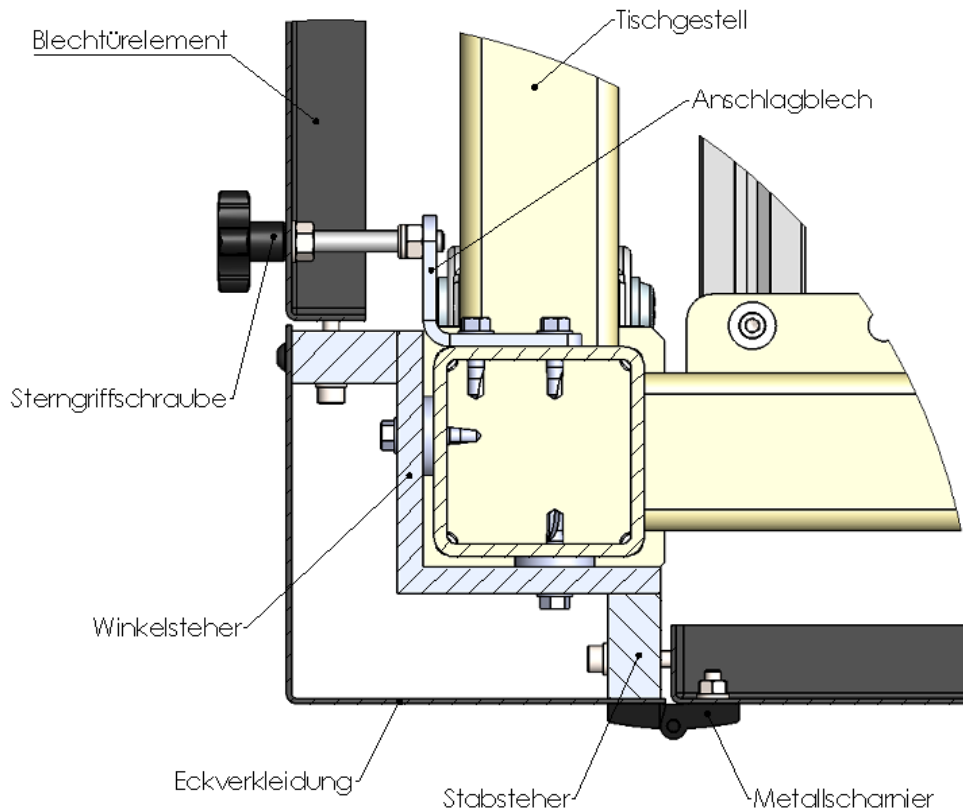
Eckkonstruktion im Detailschnitt II, Quelle: Eigene Darstellung.
